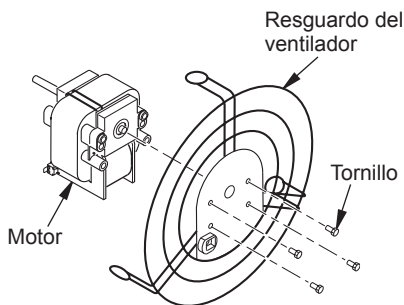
Desmontaje y montaje del resguardo del ventilador en el motor
